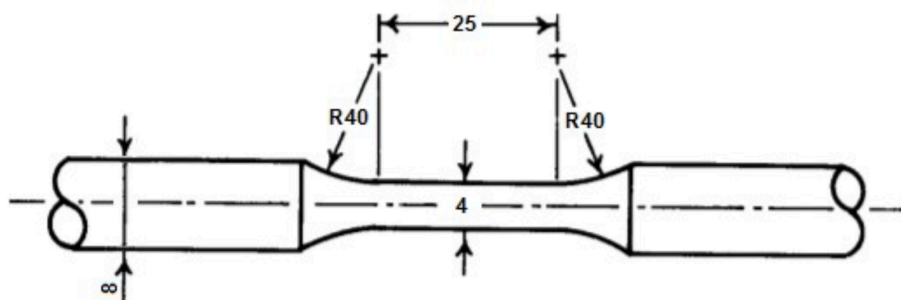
dimensões do corpo de prova (ASTM – E466-15)
